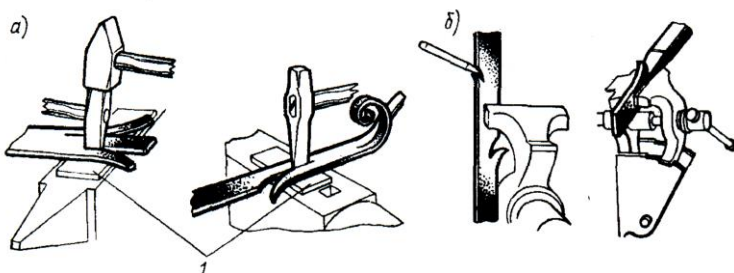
Способы разрубки и надрубки: а – на наковальне; б – в тисках; 1 – подкладка из мягкой стали или меди для предохранения зубила от затупления
